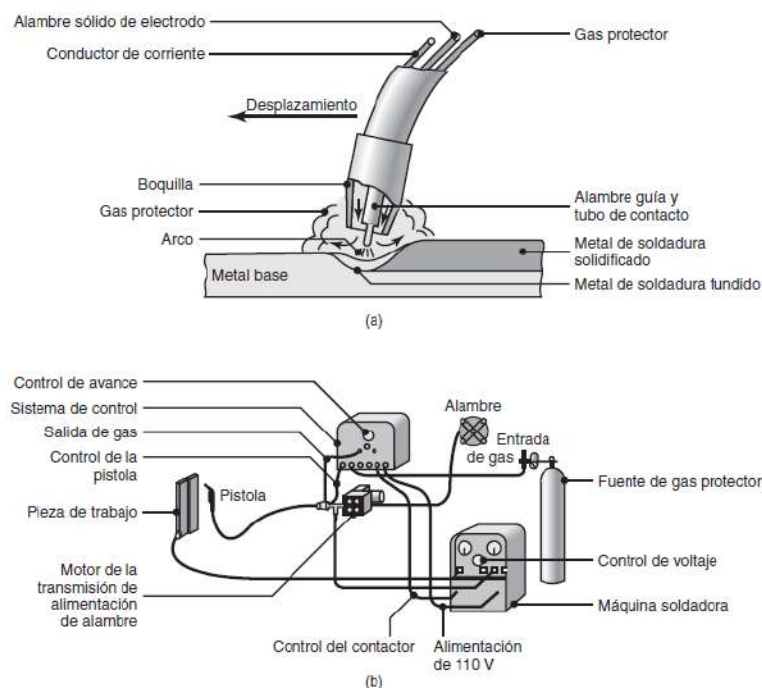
Proceso de soldadura GMAW-MIG A) Detalle del proceso de unión b) Equipo y sistema de soldadura.
